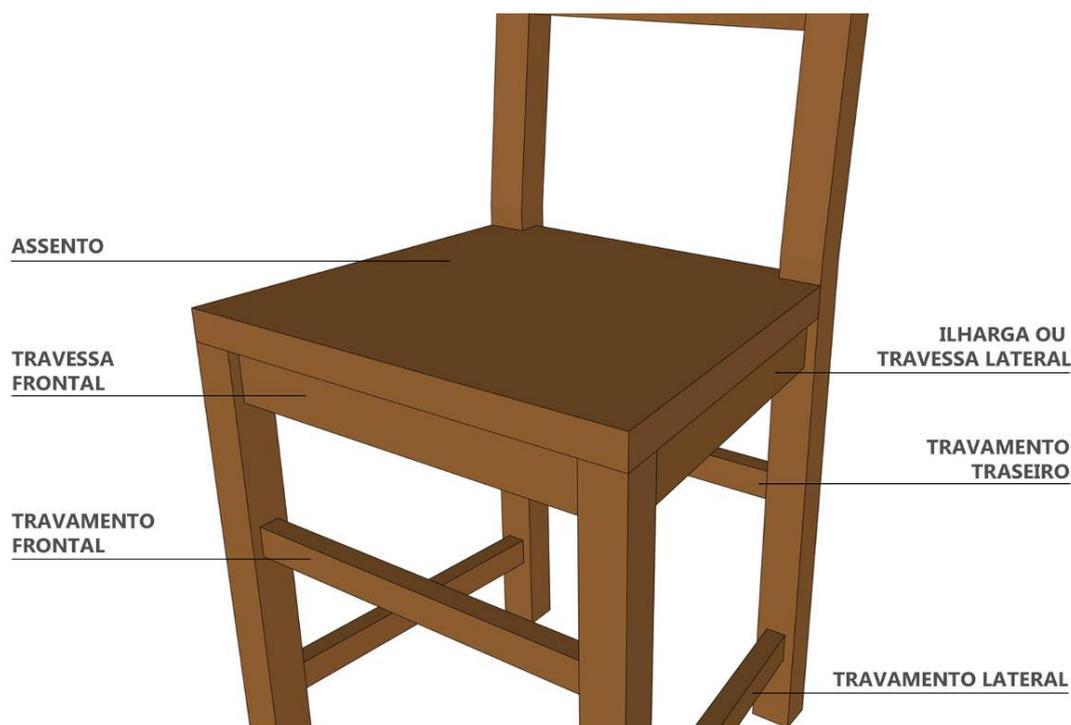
Estrutura de cadeira com travamentos inferiores.
